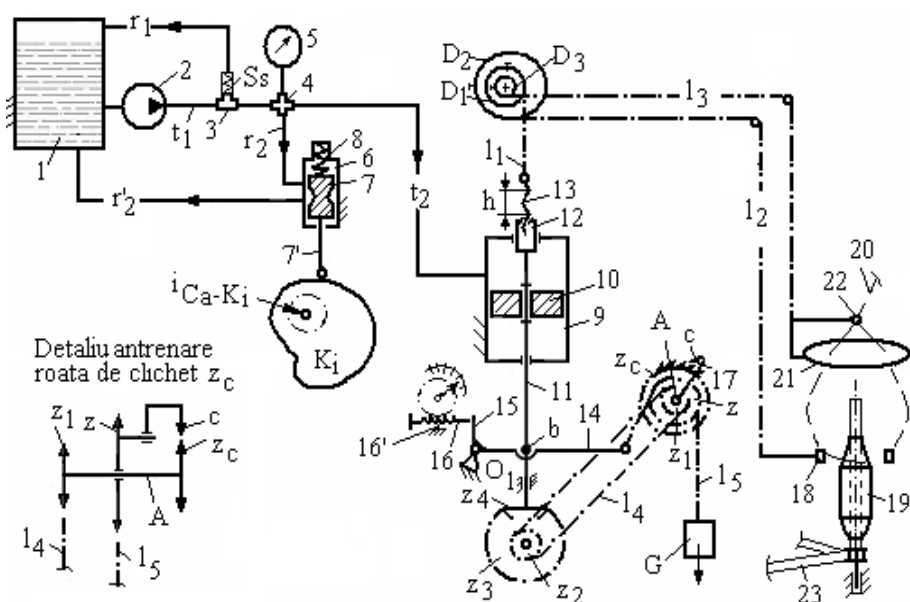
Mecanism de înfășurare cu acționare hidraulică
